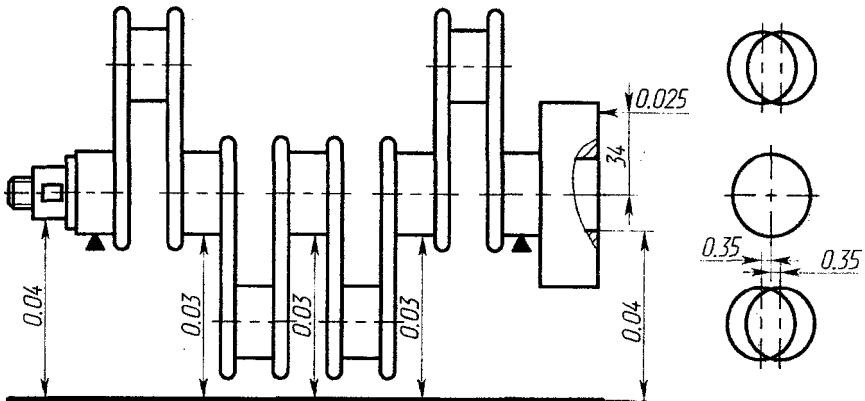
Допустимые биения поверхностей коленчатого вала
